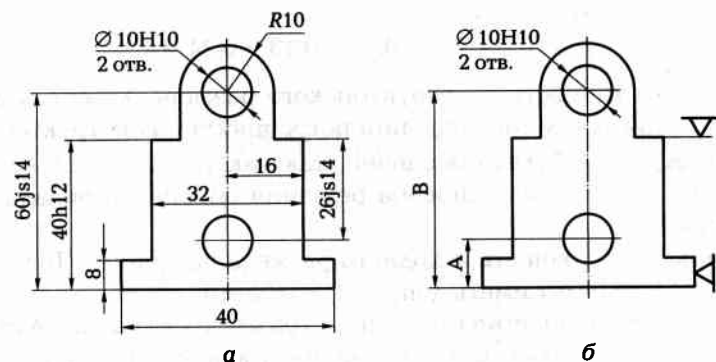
Чертеж детали (а) и схема базирования заготовки (б)
